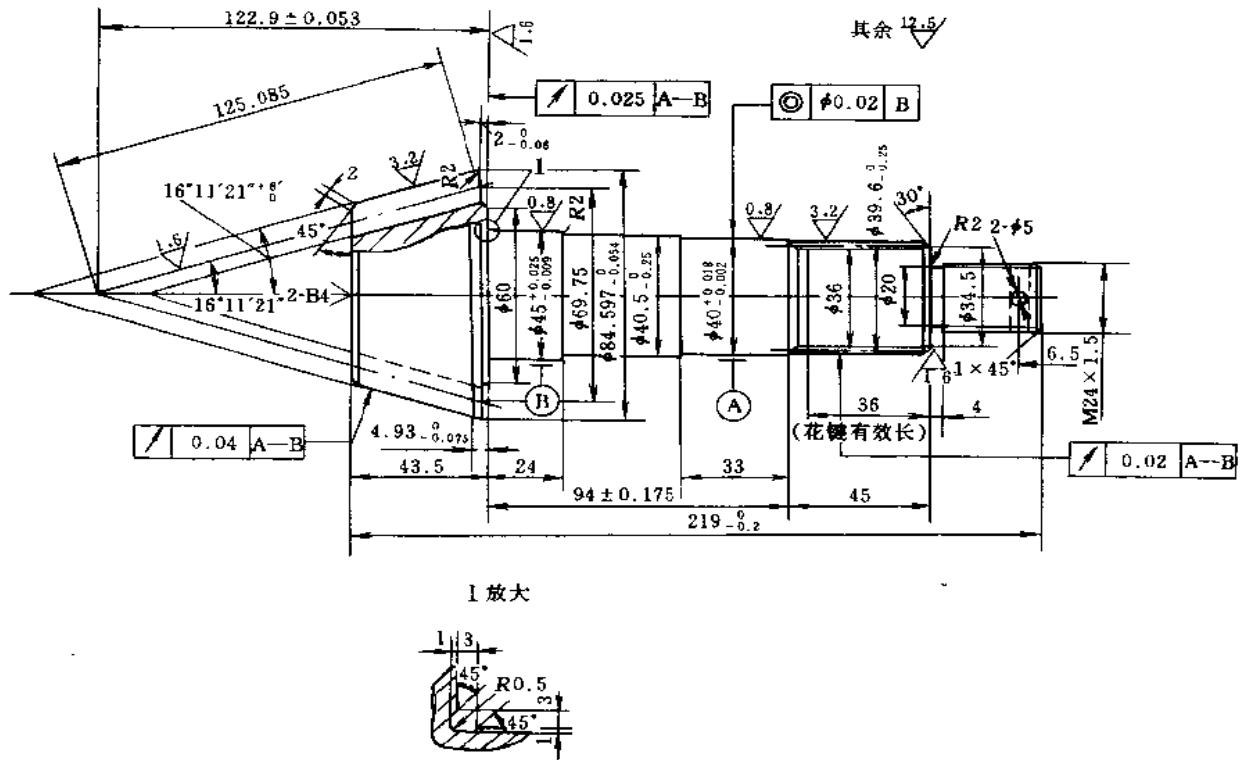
锥齿轮轴 (材料: 20CrNi2MoA)
